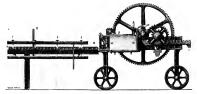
Coupe en long d'une machine à fabriquer les tuyaux de drainage.
